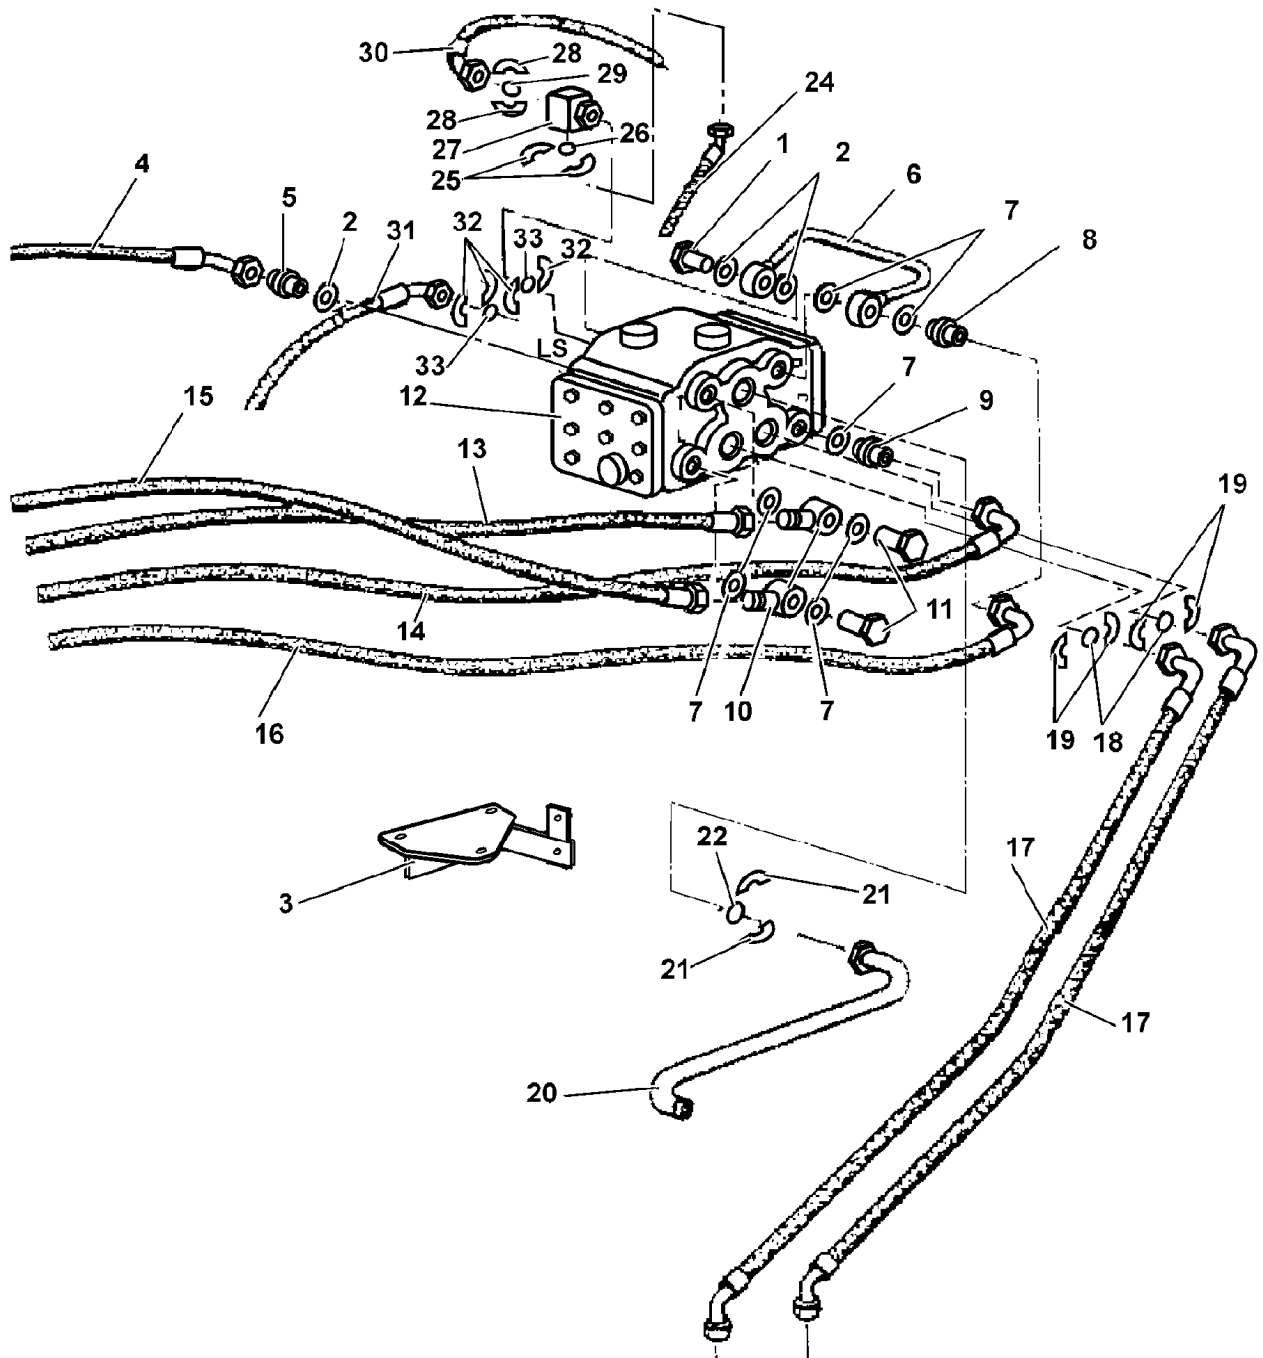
В.11. Подсоединение маслопроводов к гидроусилителю системы поворота
